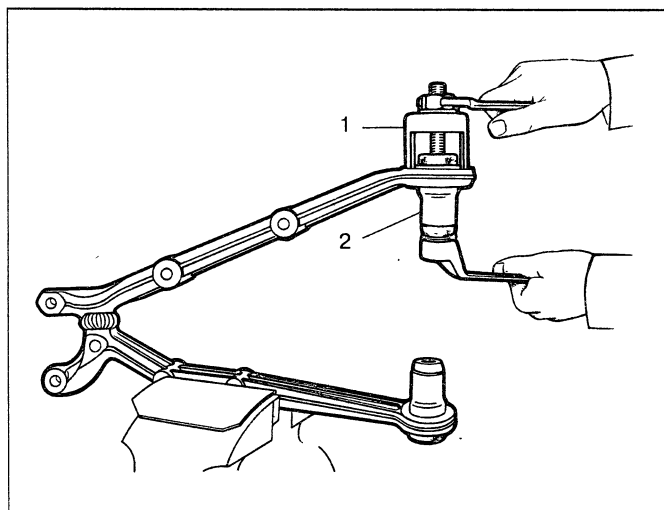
Выпрессовка шарниров нижнего рычага: 1 – приспособление 67.7823.9517; 2 – шарнир
